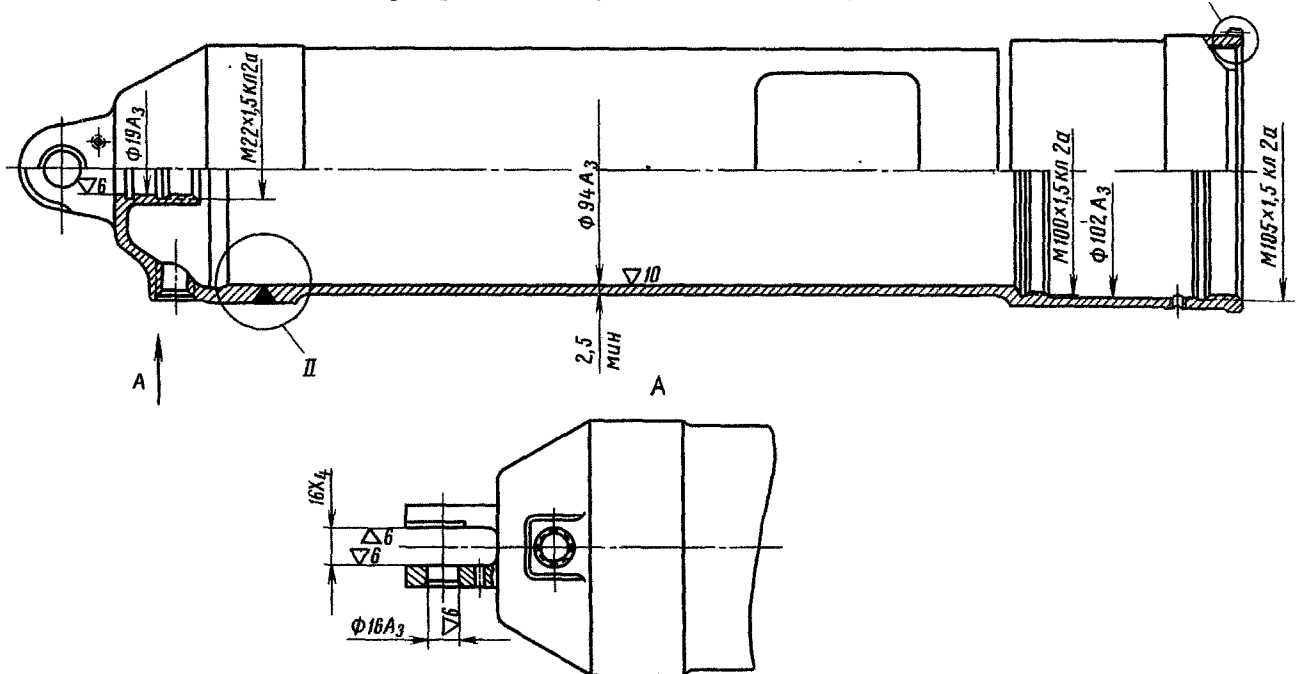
Цилиндр в сборе 8А-4101-100-А
